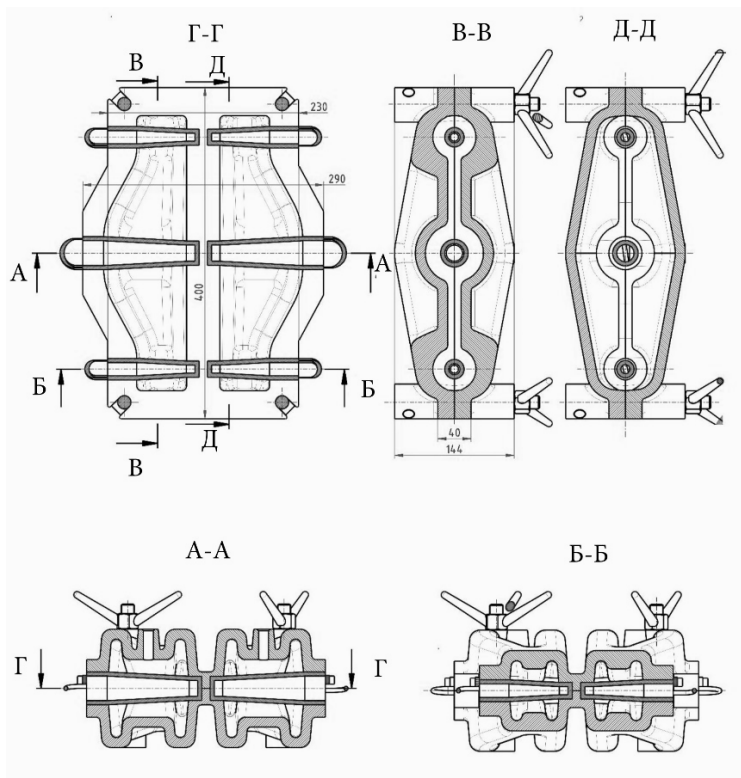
Прес-форма на виливок «Траверса»
